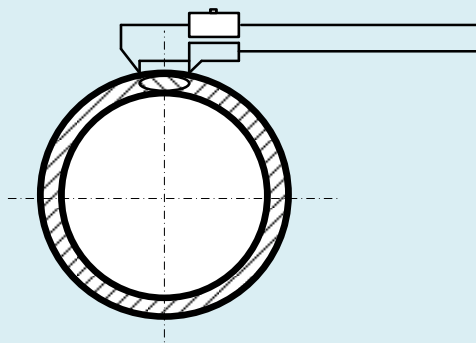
Схема измерения ширины сварных швов
